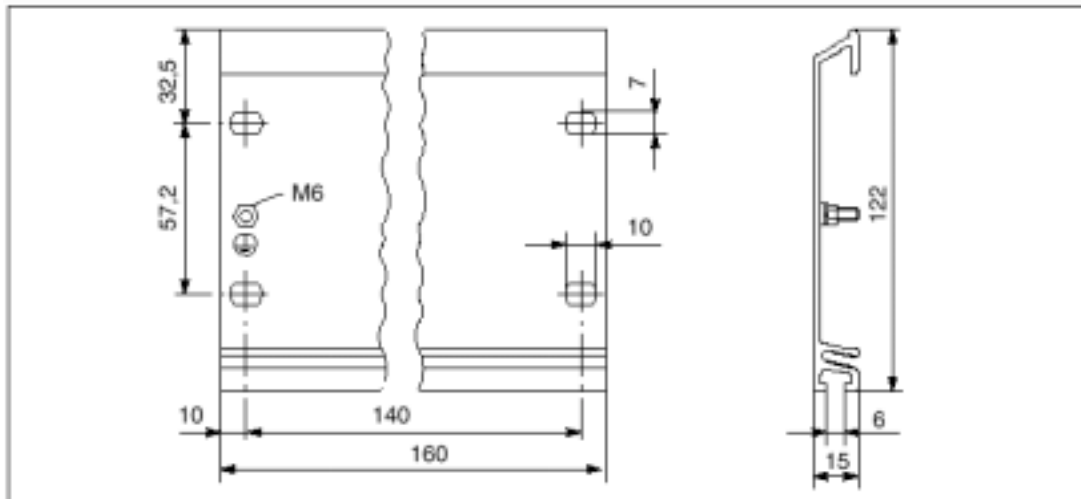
Чертеж с размерами профильной шины стандартной ширины 160 мм
